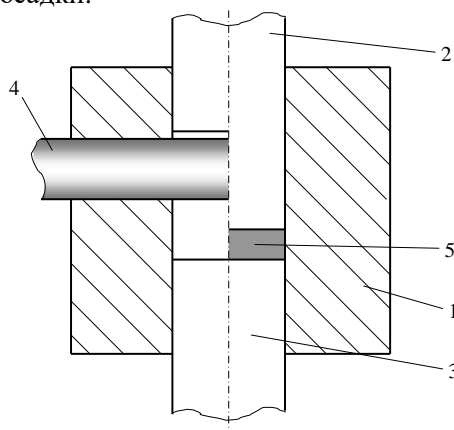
Принципова схема процесу відрізання-штампування для виготовлення циліндричних заготовок з алюмінієвого прутка: 1 - матриця, 2 - пуансон, 3 - виштовхувач, 5 - пруток, 8 – заготовка, що осаджується
